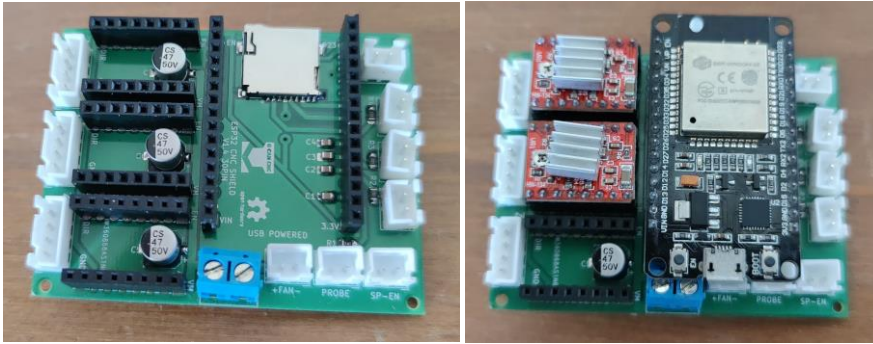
ESP32 CNC SHIELD AMB I SENSE COMPONENTS ASSEMBLATS
